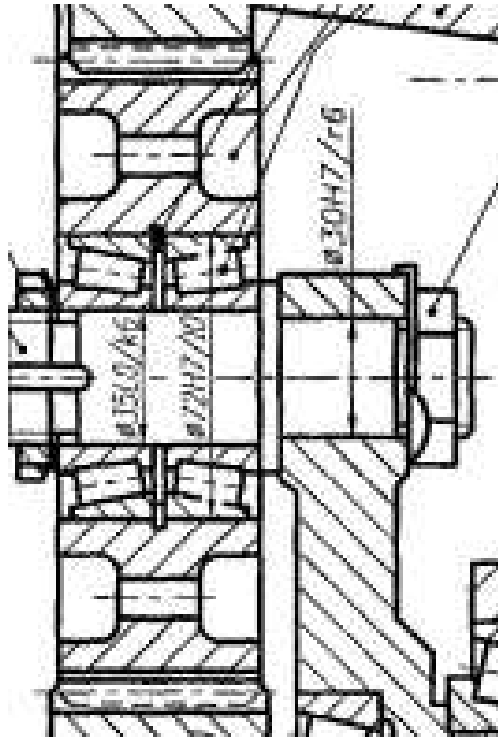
Схема установки сателлита на два роликовых подшипника, обеспечивающая большую радиальную жесткость
